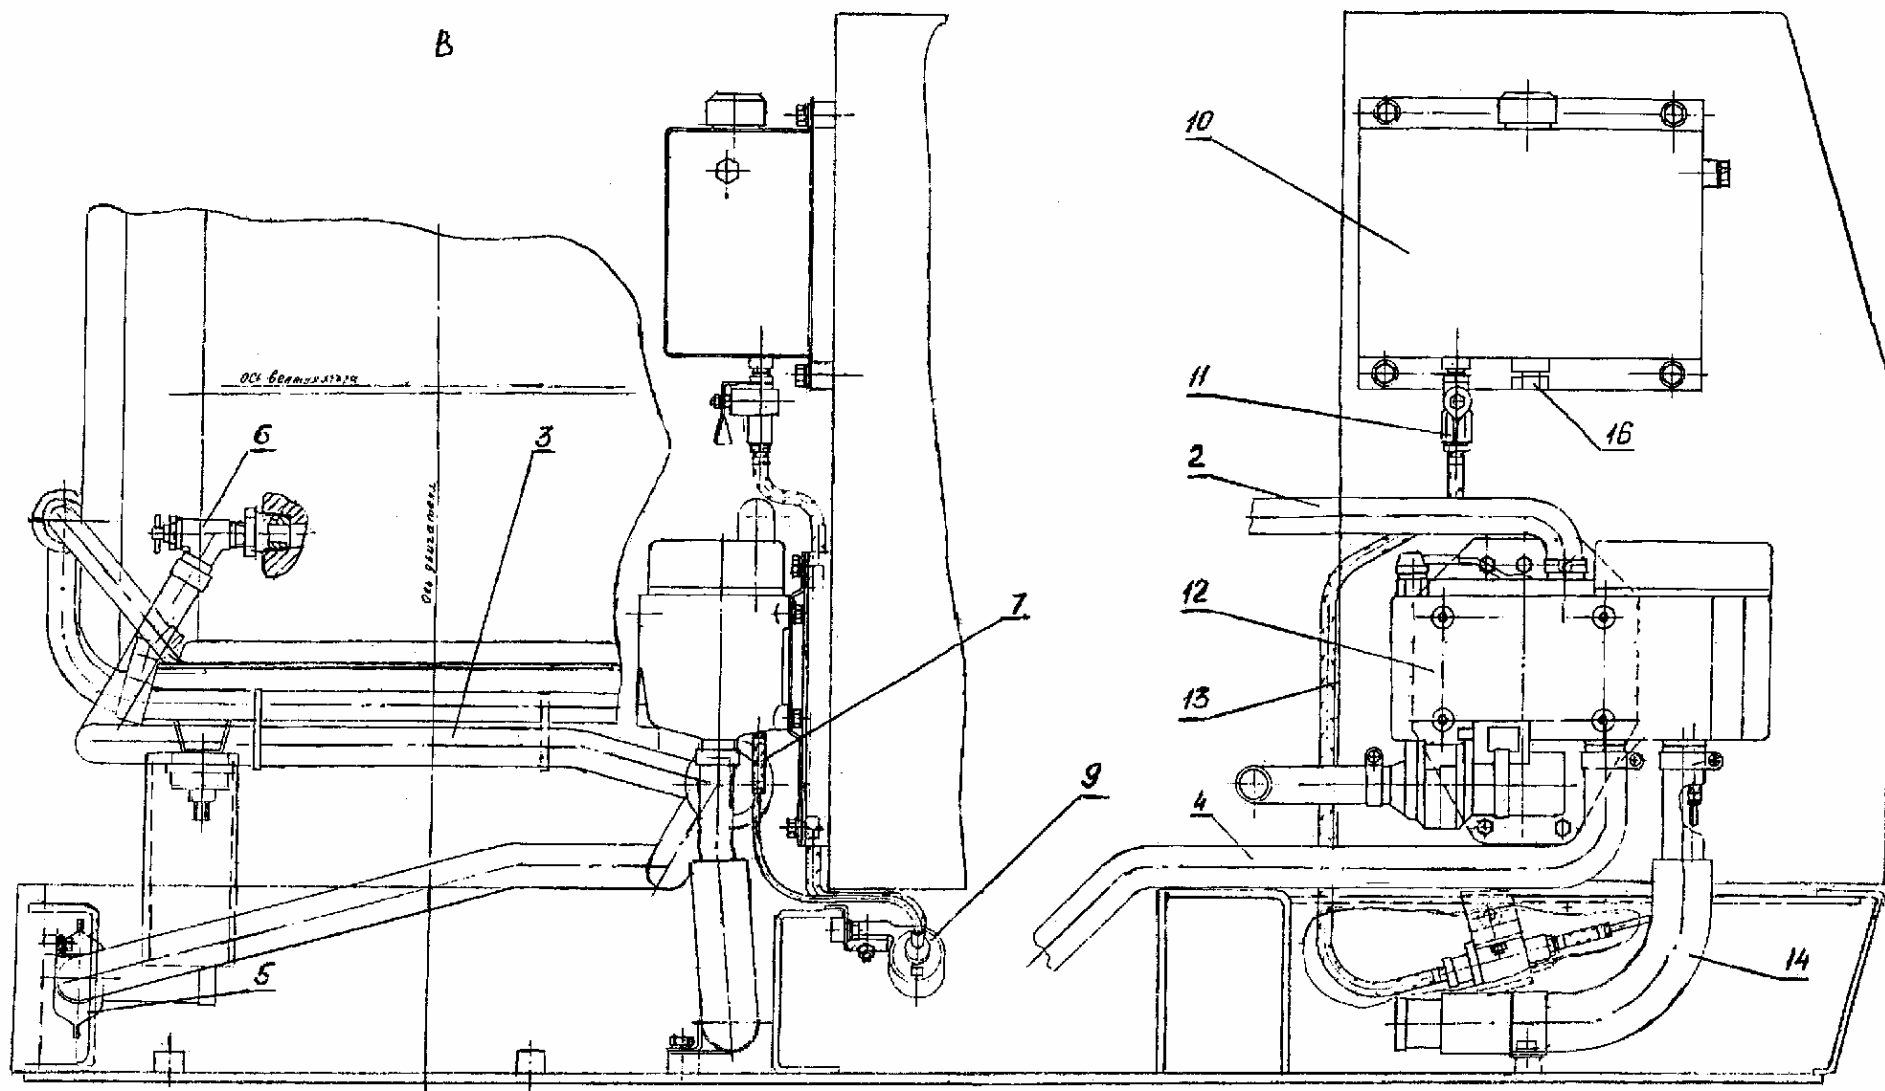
Установка предпускового подогрева двигателя и отопления кабины
